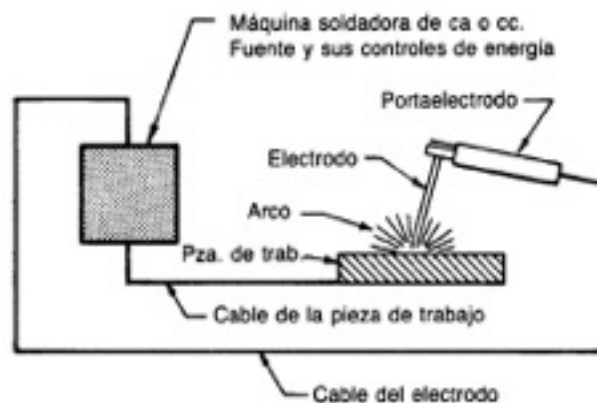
Diagrama de soldadura por arco eléctrico
